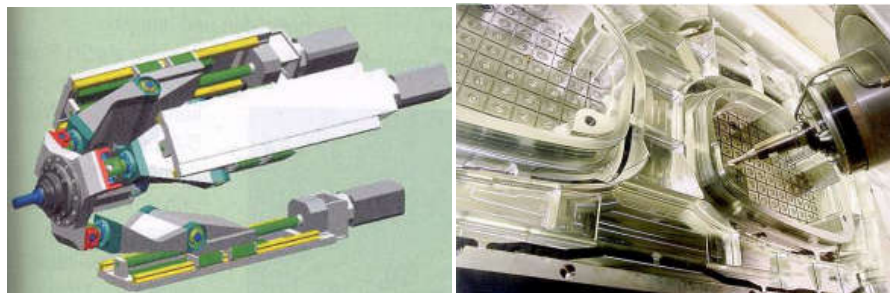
Tête d'usinage cinématique parallèle Sprint Z3 [28].
